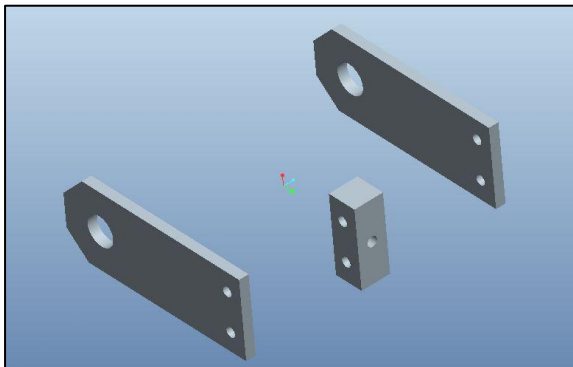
Explosionado del patín. Vista de las tres partes que lo forman.
